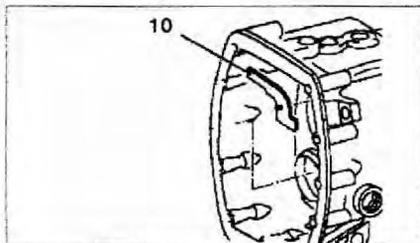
Снимите блокировочный предохранитель 10 из корпуса коробки передач.
